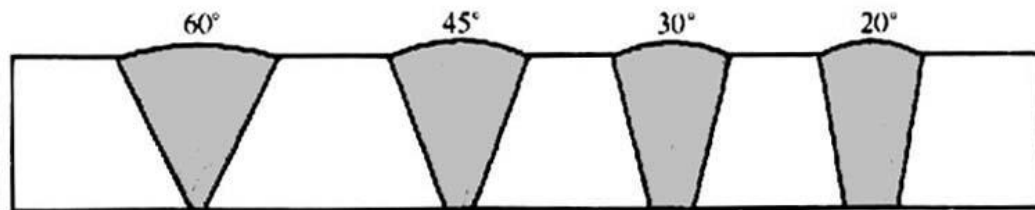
减小根部间隙和坡口角度可以减少焊缝金属和焊接时间
